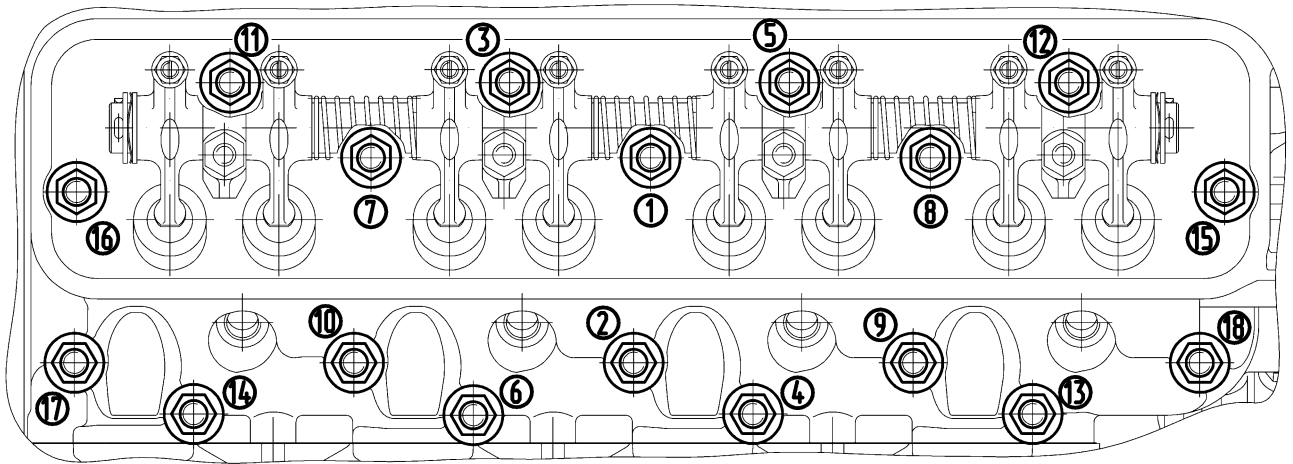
Порядок подтяжки гаек крепления головок цилиндров
